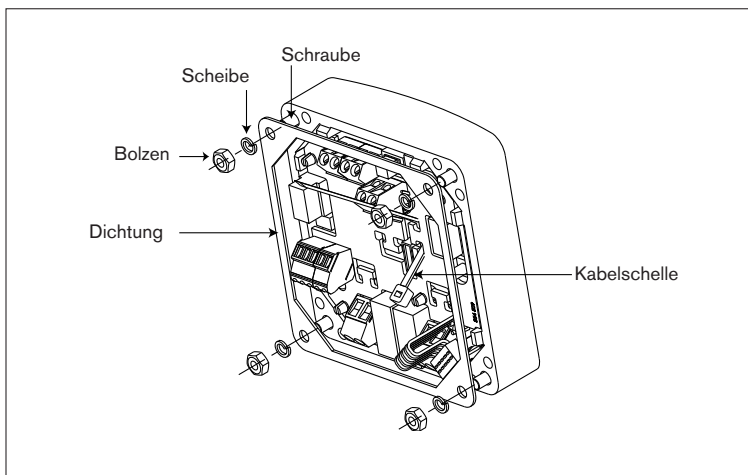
Installation pH-Transmitter 8205, Schaltschrank-Ausführung
